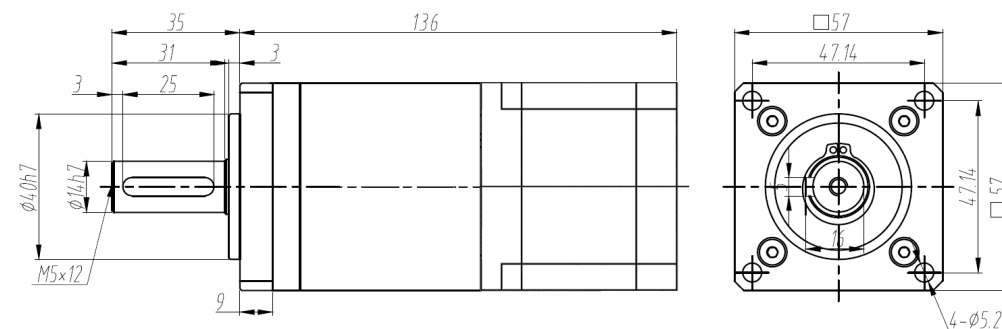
Габаритные и присоединительные размеры ШДР57-2,8-9-1/25
